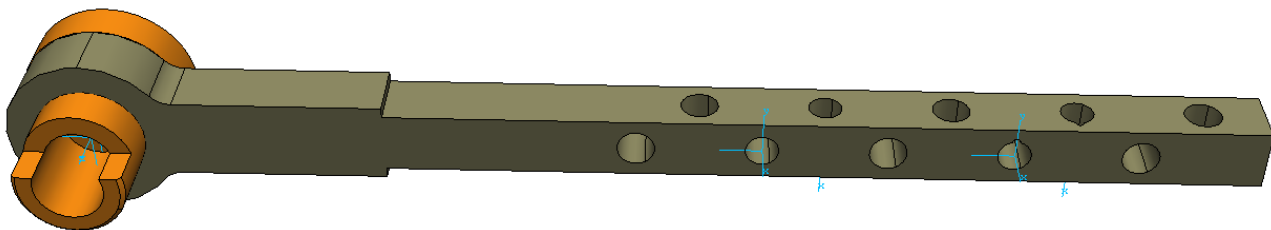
Калибровочный инструмент для сварочного пистолета
